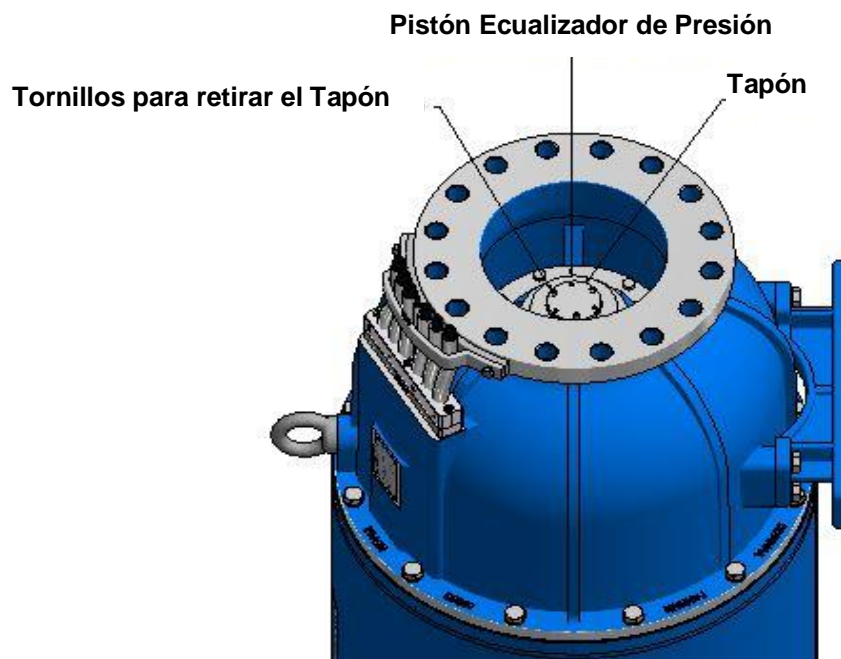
Detalle del Pistón Ecualizador de Presión.
